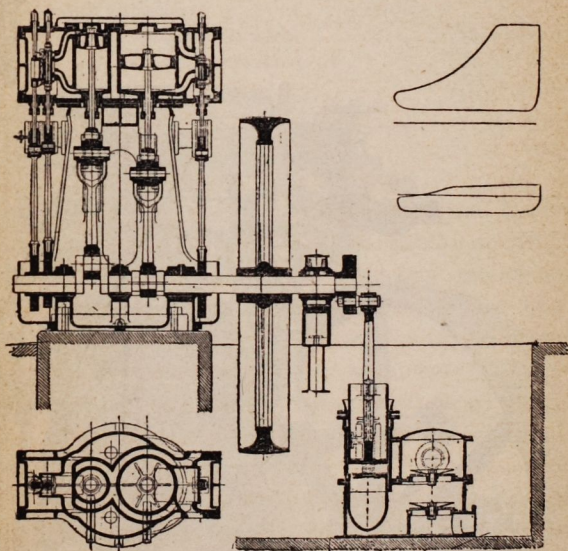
Coupe de la machine Buffaud et Robatel.
